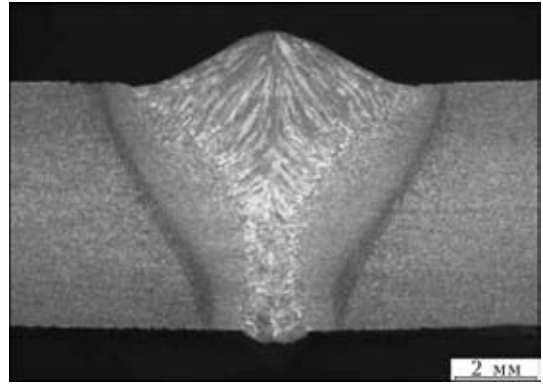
Макрошлиф сварного соединения, полученного гибридной лазерно-дуговой сваркой
